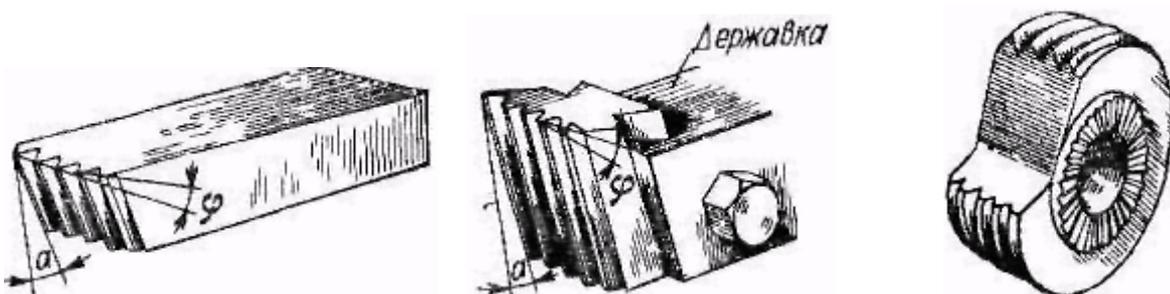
Многониточные резьбовые резцы (гребенки)
